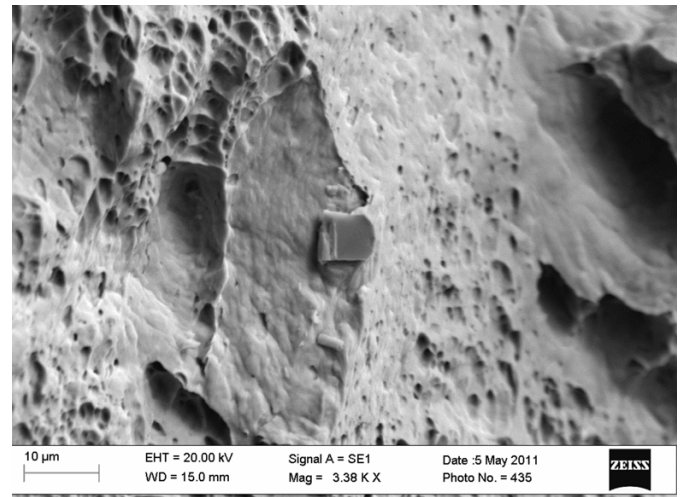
Отдельная частица хрупкой фазы, имеющая кубическую форму, на поверхности излома сварного шва стали 12X18H10T
